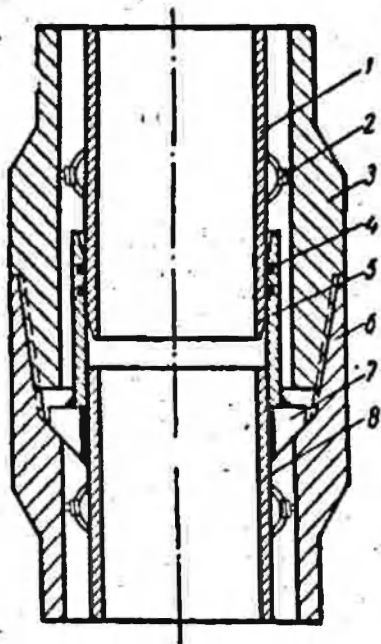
Конструкция двойной колонны бурильных труб с пружинными центраторами
